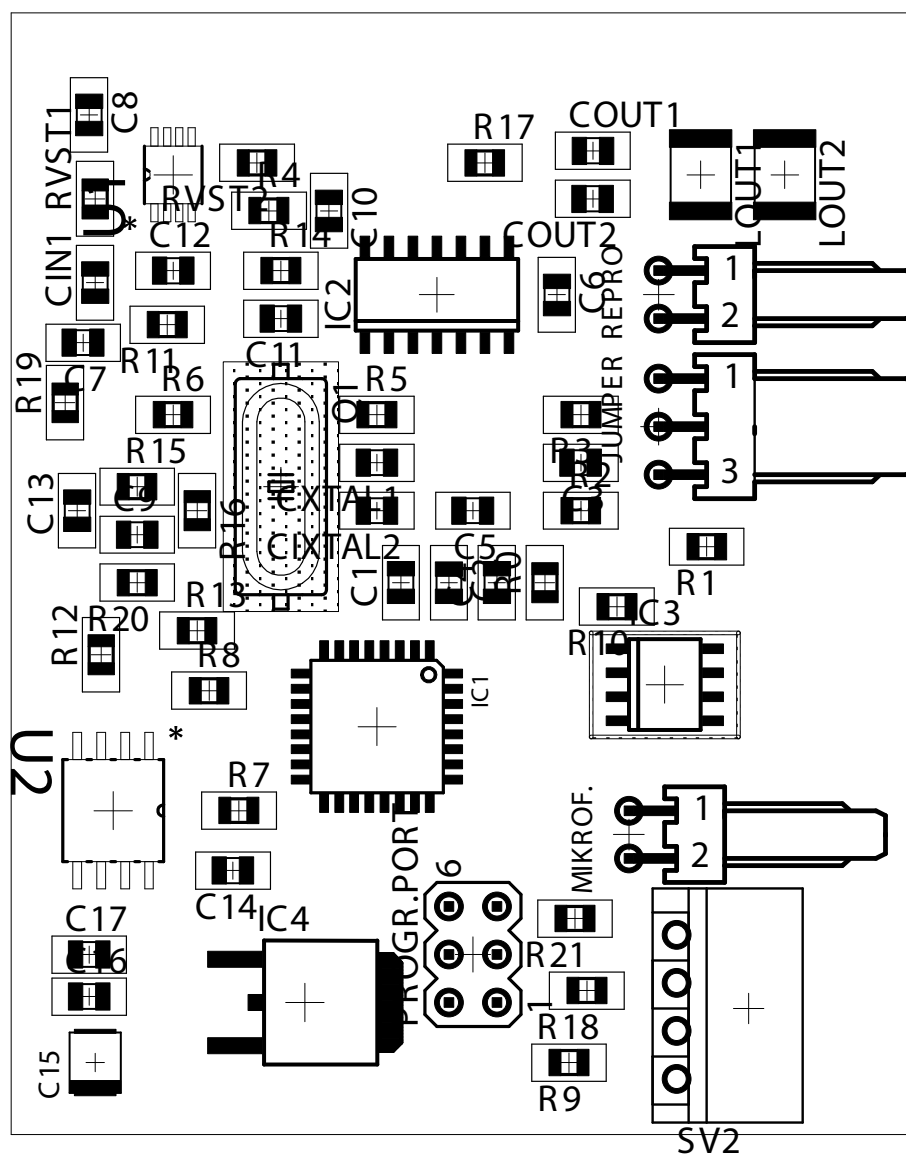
Rozměr desky 62 x 53 [mm], Měřítko M=1.5:1
